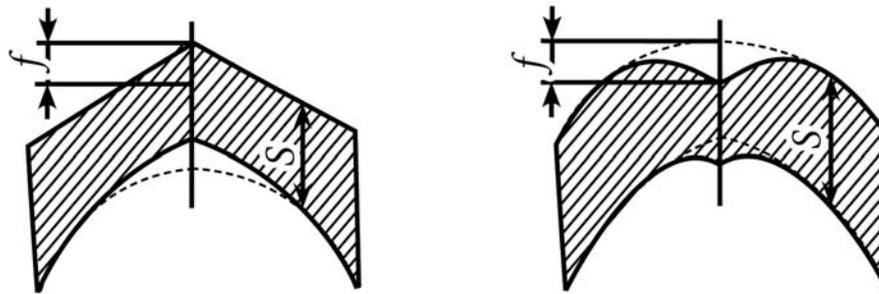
Увод (угловатость) кромок в сварных швах
